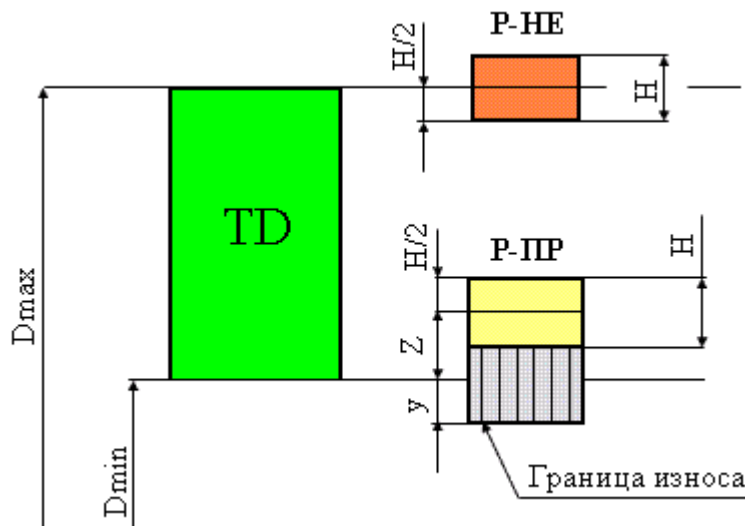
Схема расположения полей допусков калибров для отверстий IT6-IT8
